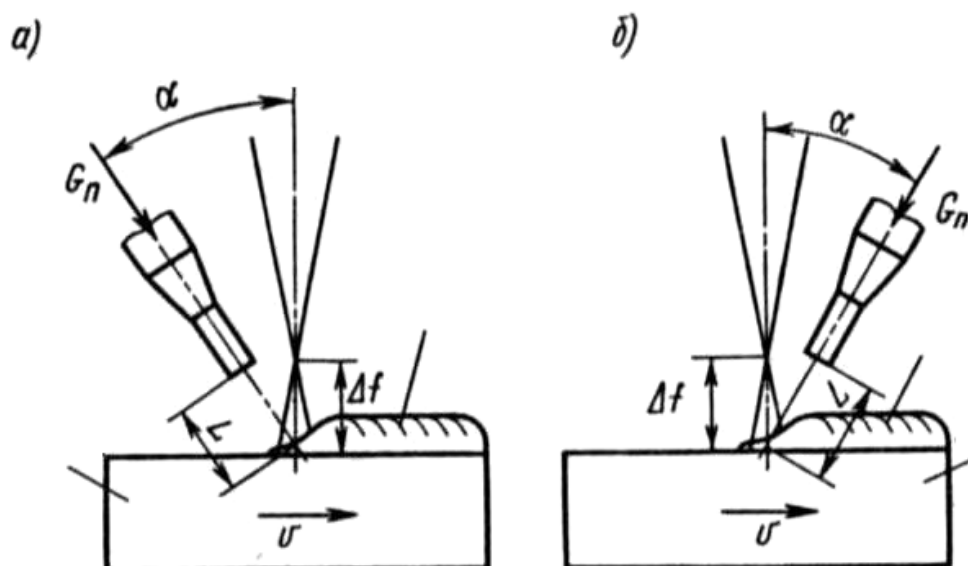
Схема газопорошкового лазерного наплавлення з подачею порошку [14]
